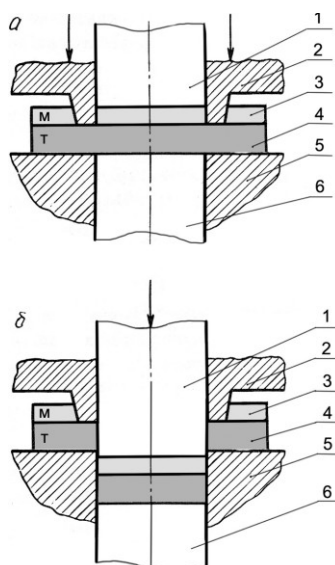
Схема чистовой вырубki встречными матрицами
